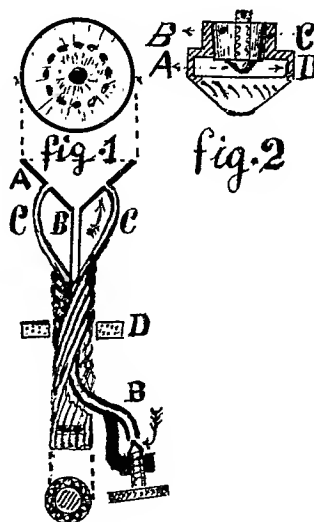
A, stator conique de 90° d'angle; B, conduit permettant par vis-pointeau le réglage d'arrivée d'air; C, tuyère; D, anneau de caoutchouc mousse. — Fig. 2 : A, vis du couvercle du rotor; B, couvercle du rotor; C, paroi cylindrique du rotor; D, gorge dans la cavité du rotor.
